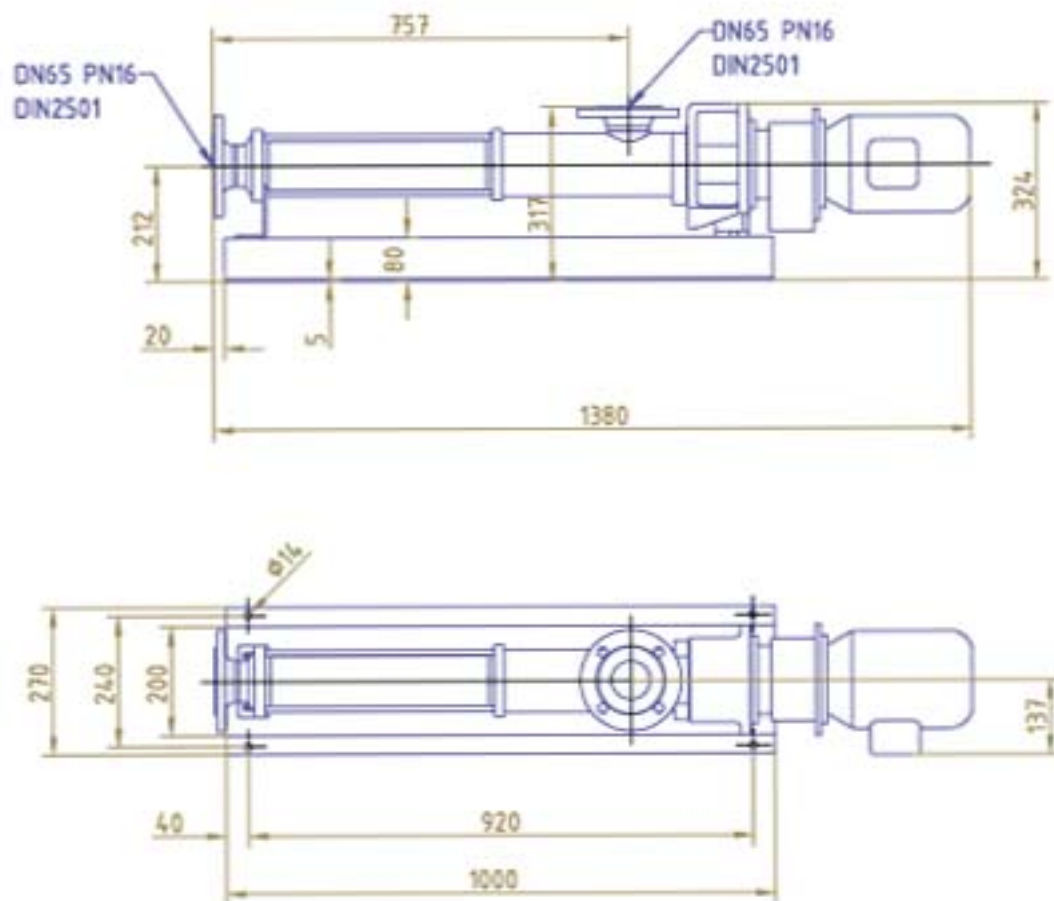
Габаритный чертеж насоса КРК70АР001
